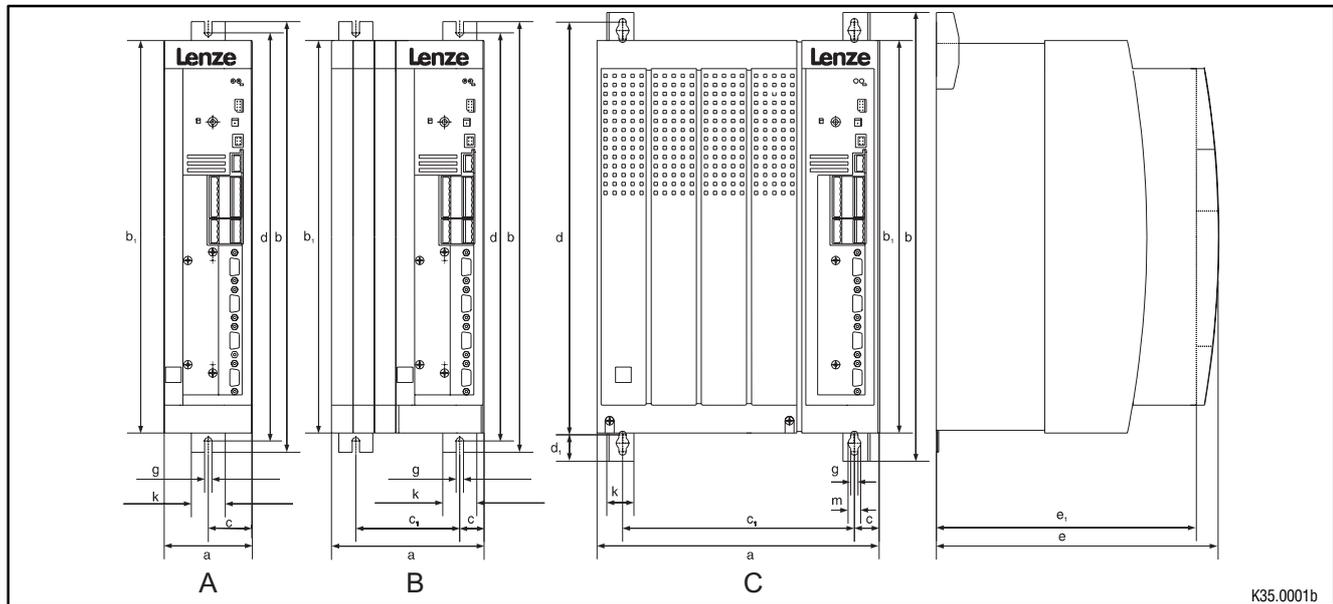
Dimensionado para el montaje accesorios de sujeción
